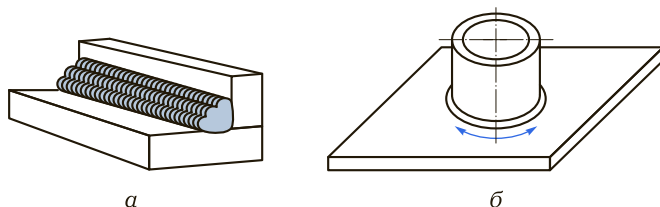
Положение при сварке тавровых швов:
